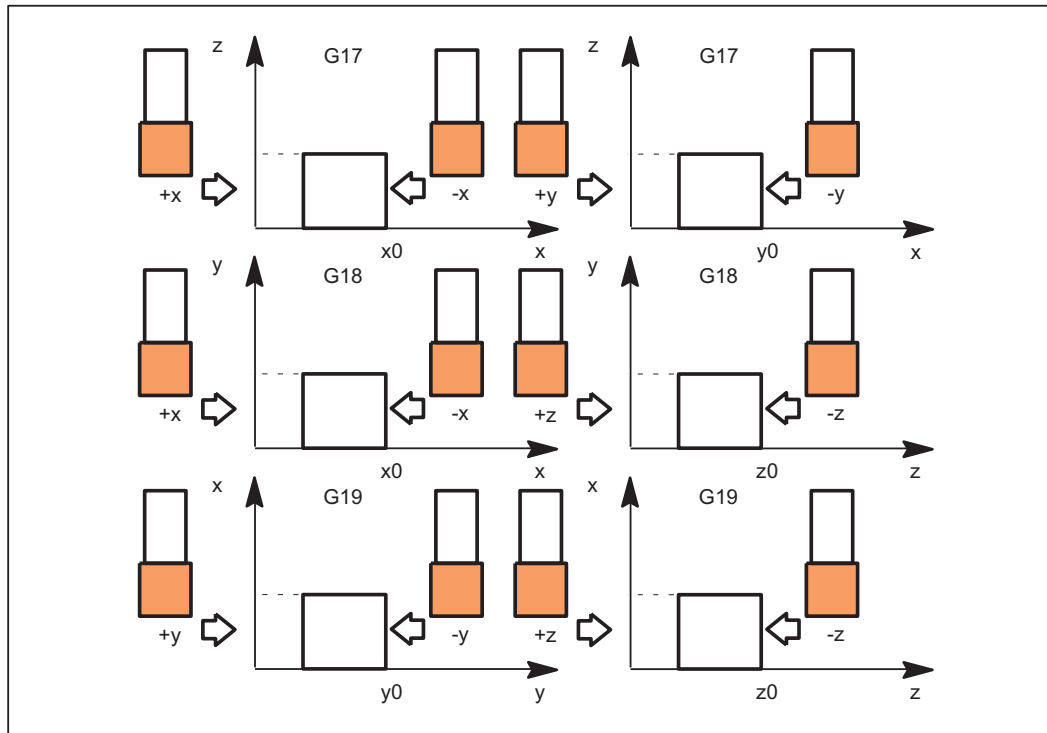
Werkzeugdurchmesser für die ausgewählte Ebene G17, G18 und G19
